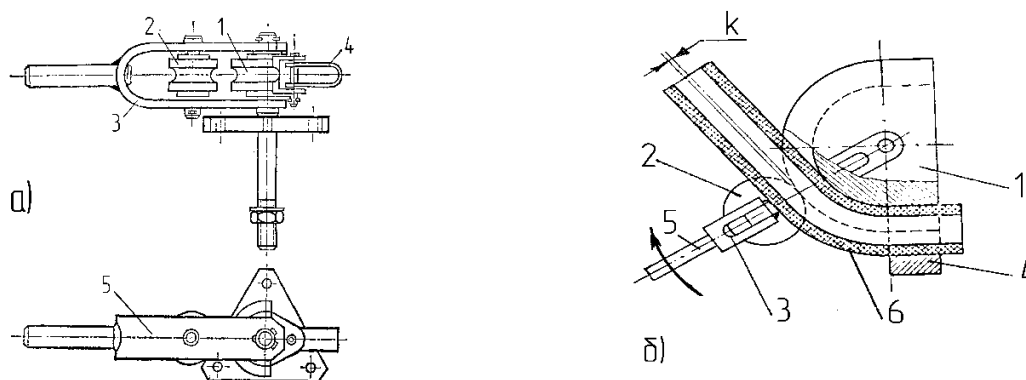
Станок для гибки труб с ручным приводом: а) - общий вид; б) - схема гибки: 1 - неподвижный шаблон; 2 - гибочный ролик; 3 - скоба; 4 - зажим; 5 - рычаг; 6 - изгибаемая труба
